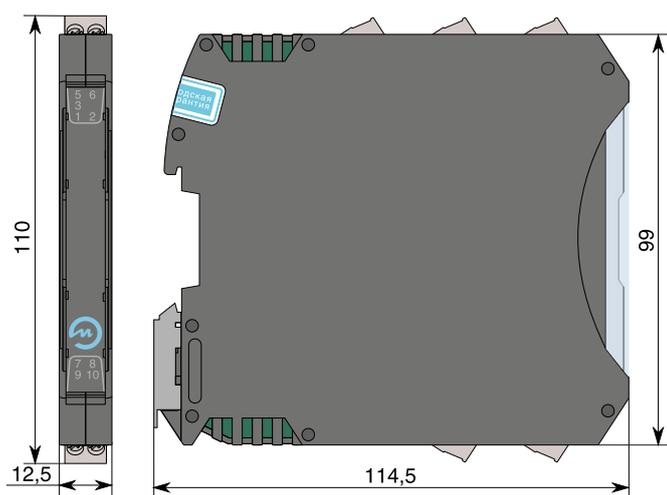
Габаритные размеры модуля в корпусе шириной 12,5 мм с разъемами с винтовыми клеммниками
